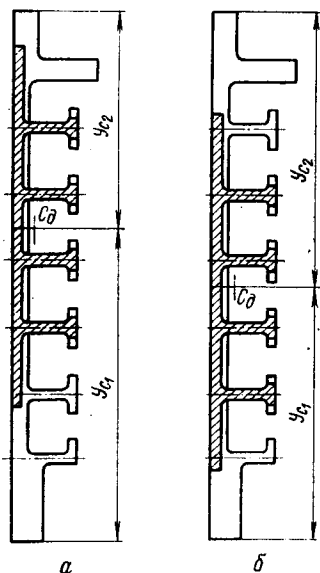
Схема вписывания сечения детали в сечение заготовки:
